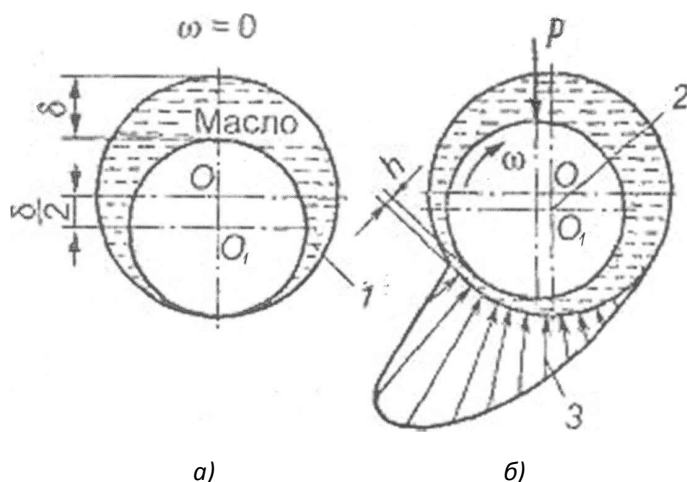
Положение цапфы вала смесителя в подшипнике:
